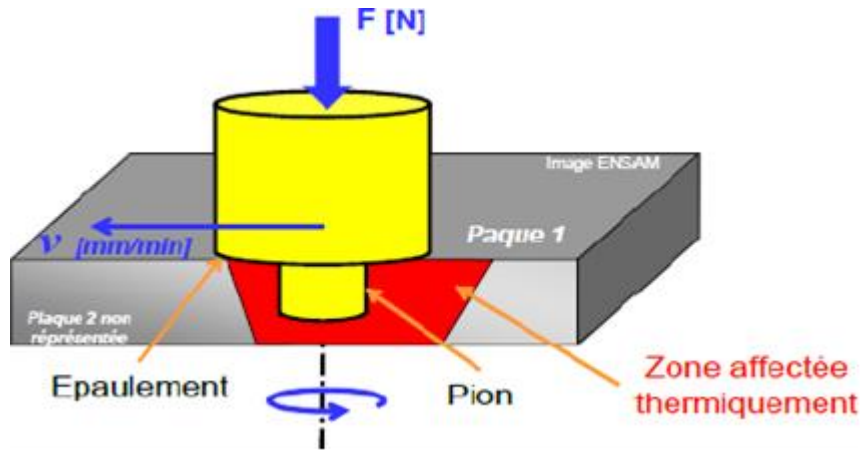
Visualisation des paramètres de soudage [21].
